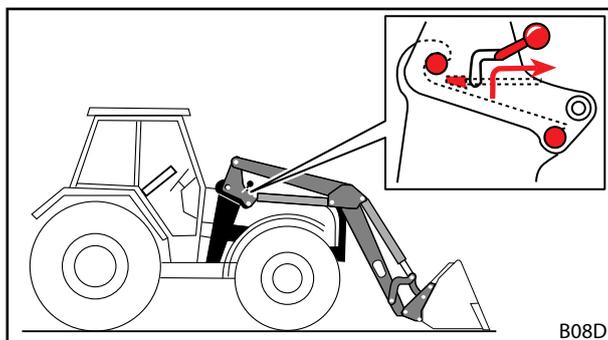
Allentare il dispositivo per il bloccaggio del caricatore frontale
